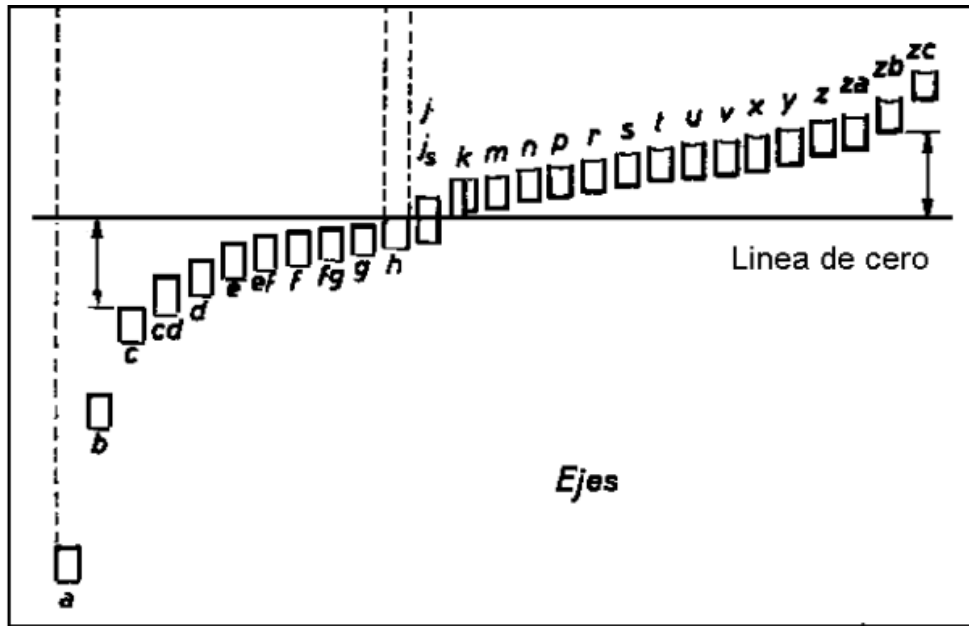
Posición de la zona de tolerancia para ejes (ANSI, 2004.)
